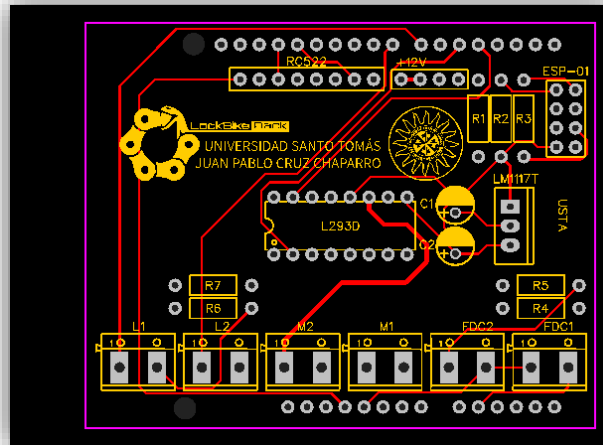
Diseño capa superior PCB, Proteus 8 Profesional – LockBikeRack
